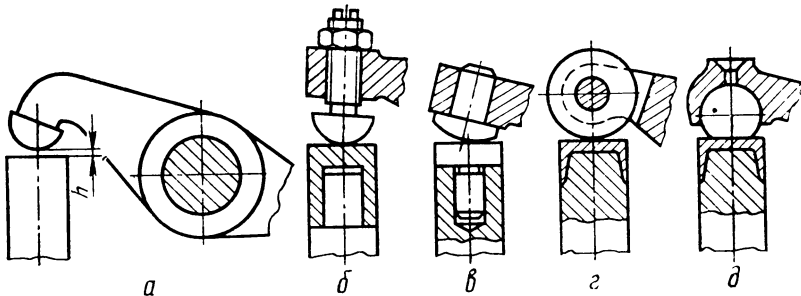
Последовательное упрочнение конструкции привода возвратно-поступательного движения штока
